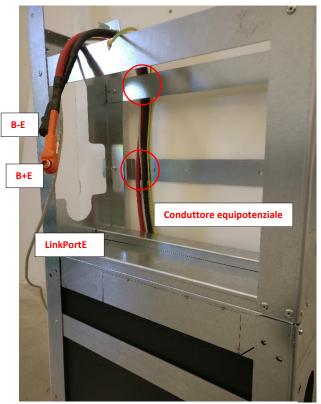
Posa conduttori di collegamento tra WALL-BOX-Bx BASE e WALL-BOX-Bx ESPANSIONE
